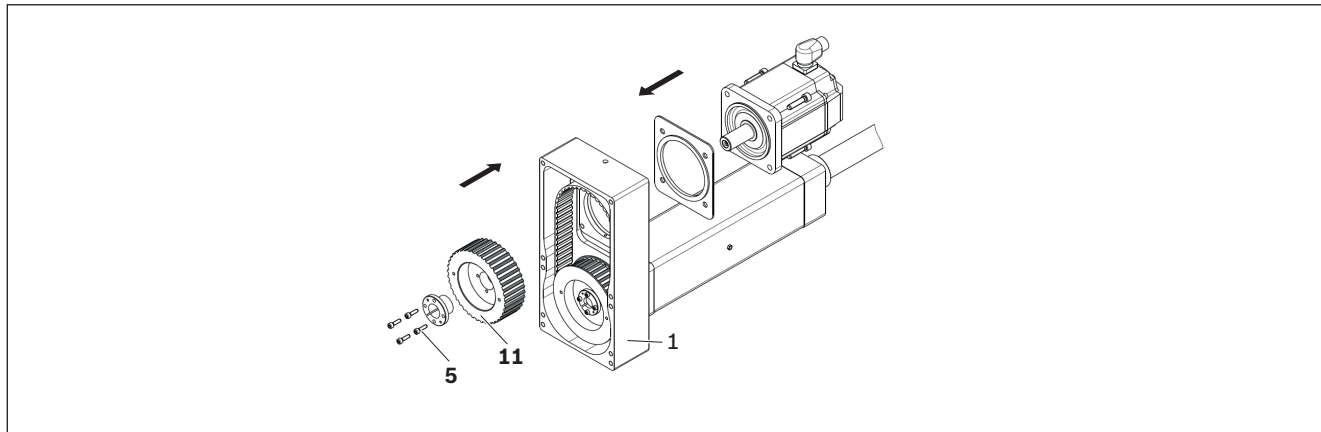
Montage du moteur et de la poulie côté moteur, $i = 1$
